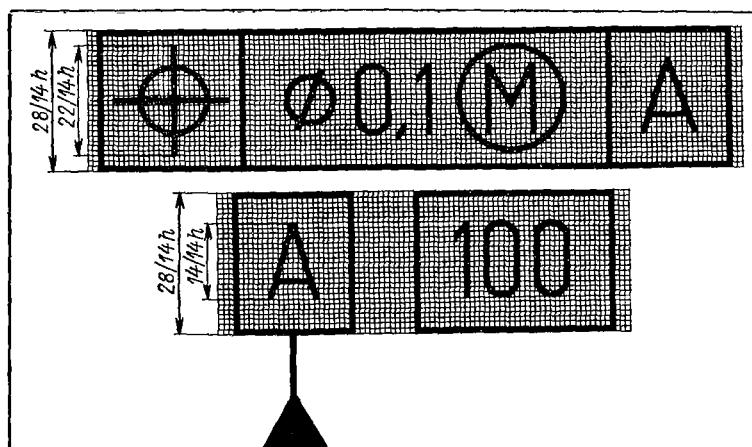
Размеры обозначений допусков в рамке
